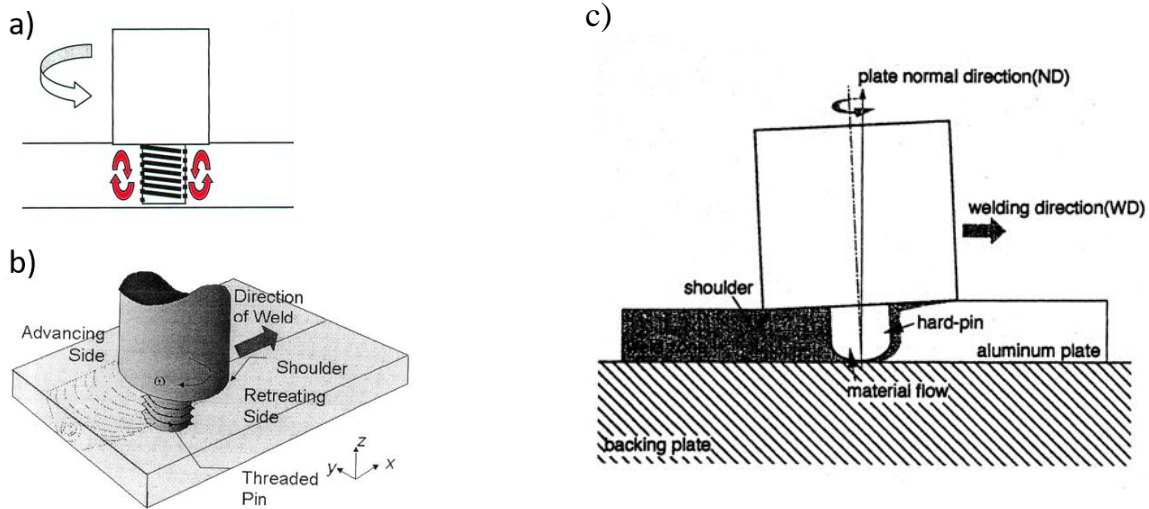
Représentation du soudage FSW (Friction Stir Welding). a) Drainage en profondeur de la matière grâce au filetage du pion. b) Schéma du procédé de soudage FSW : vue au-dessus.<sup>11</sup> c) Schéma du procédé de soudage FSW : coupe parallèle.<sup>12</sup>
